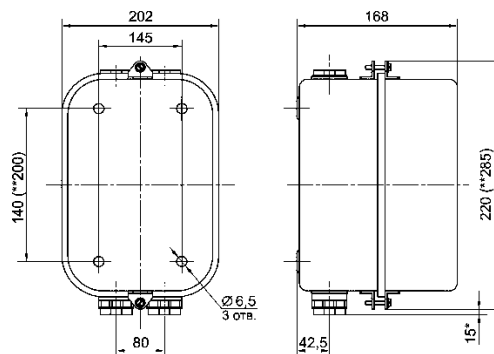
Пускатель ПМ12-063 63А в защитном корпусе. - IP40; IP54
